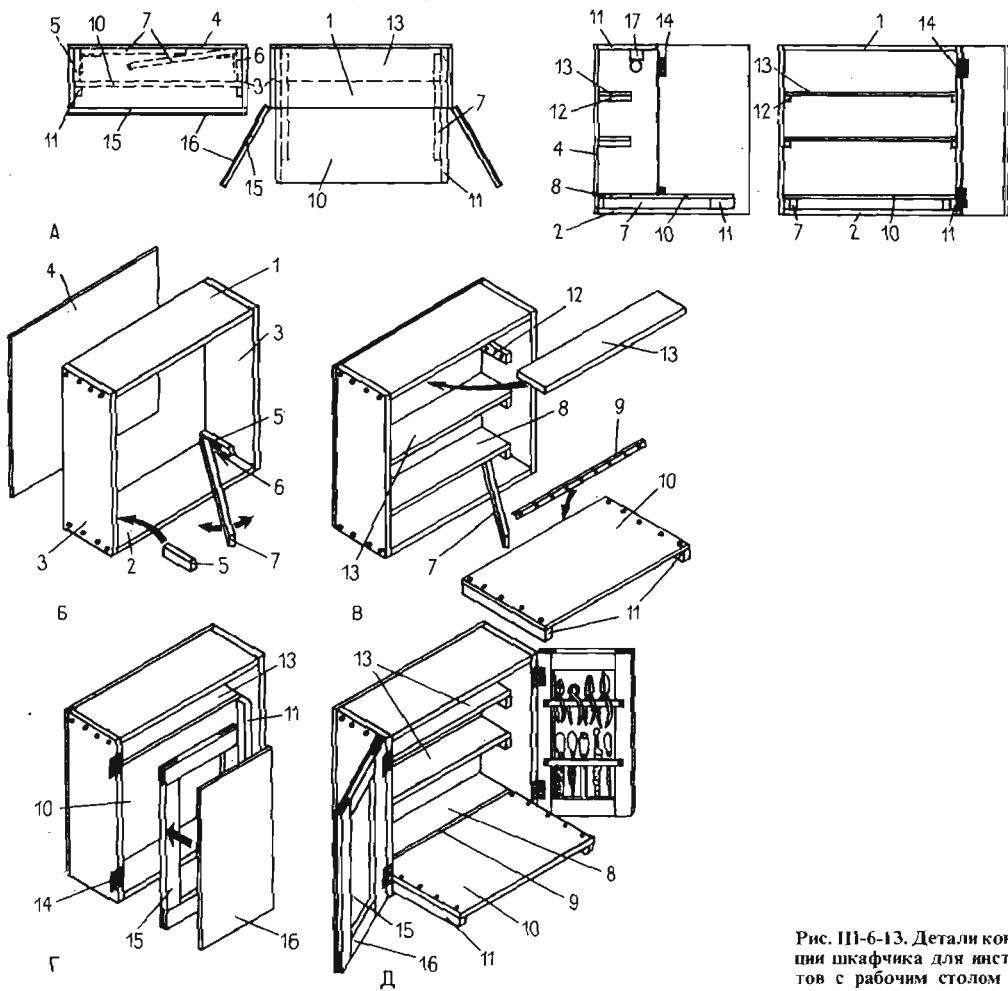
Детали конструкции шкафчика для инструментов с рабочим столом
